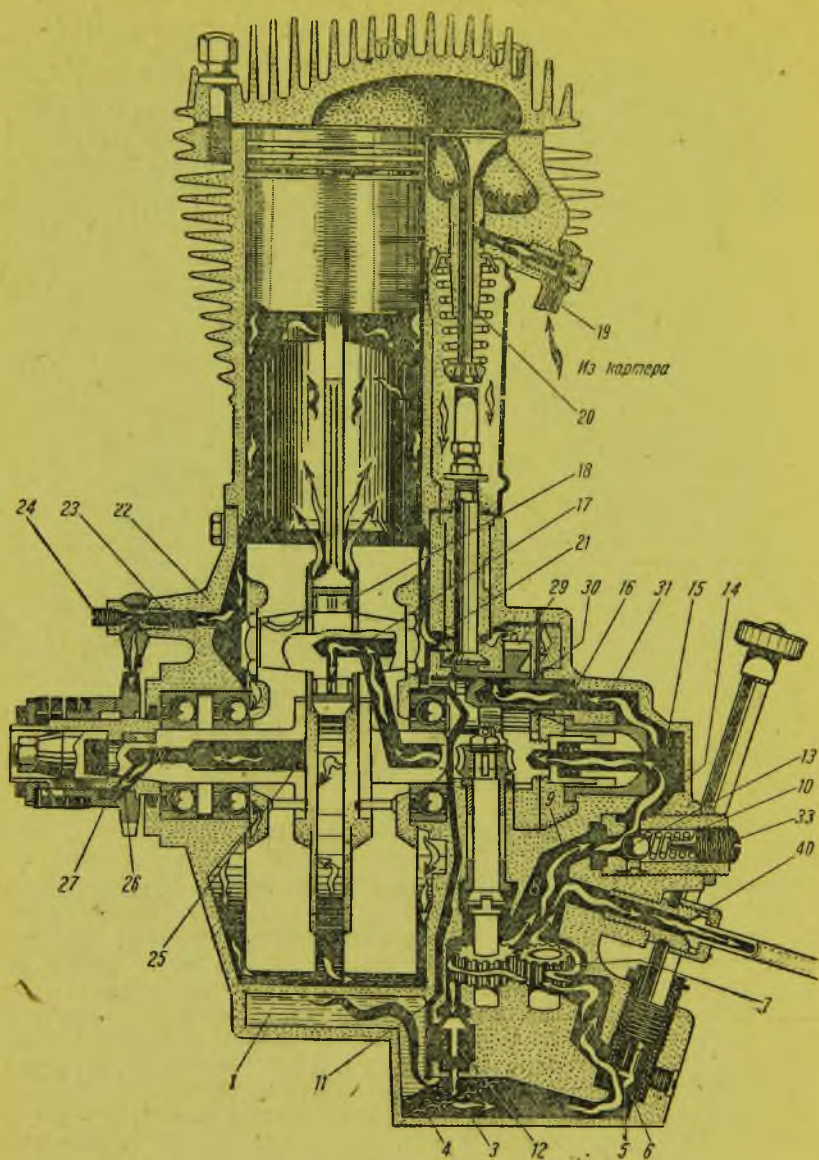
а. Схема смазки двигателя ТИЗ-АМ-600
